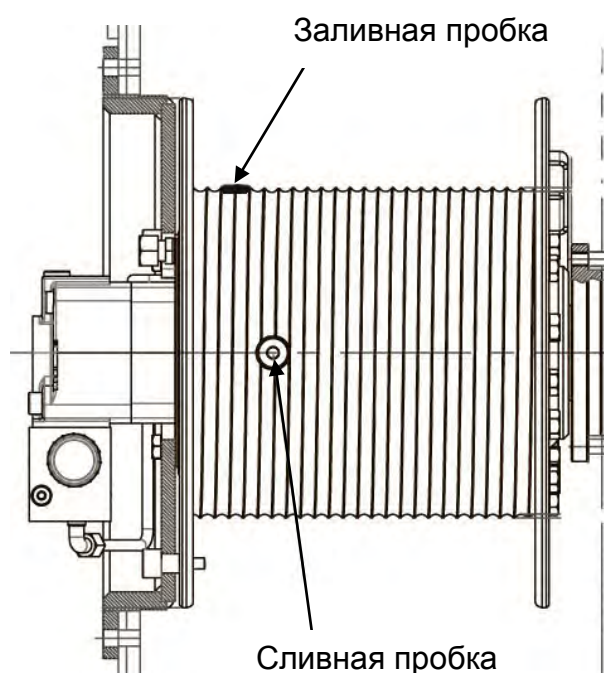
Лебедка с расположением сливной и заливной пробок на рабочей цилиндрической поверхности барабана
